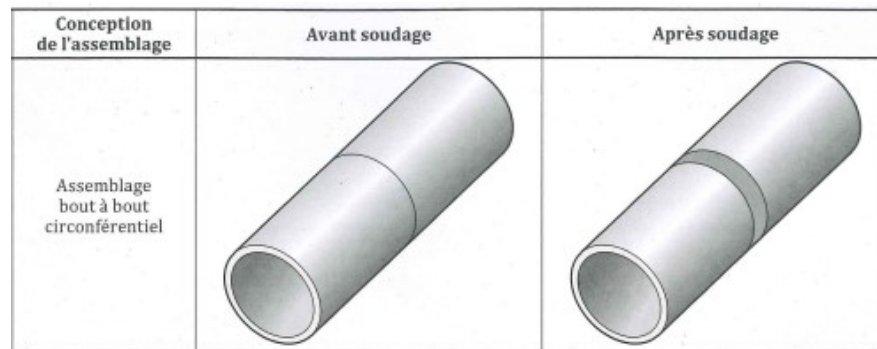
Types de joint soudé bout à bout (suite) [20]
